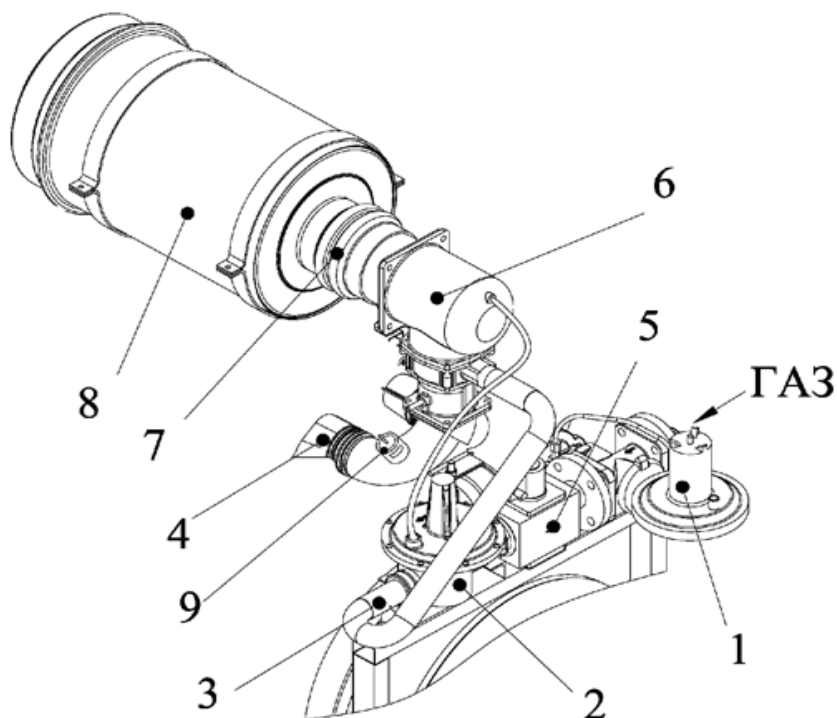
устройство газоборудования электроагрегата АПК250С:
